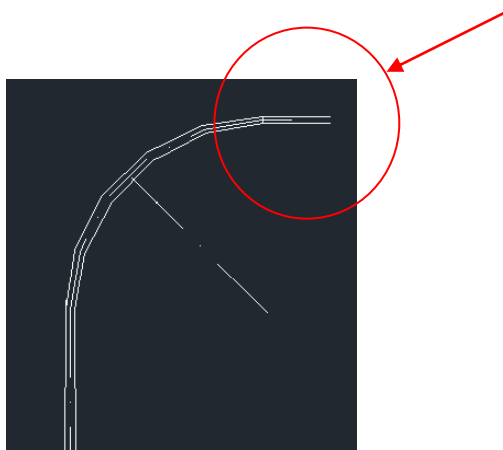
Soldadura del casquillo al báculo
